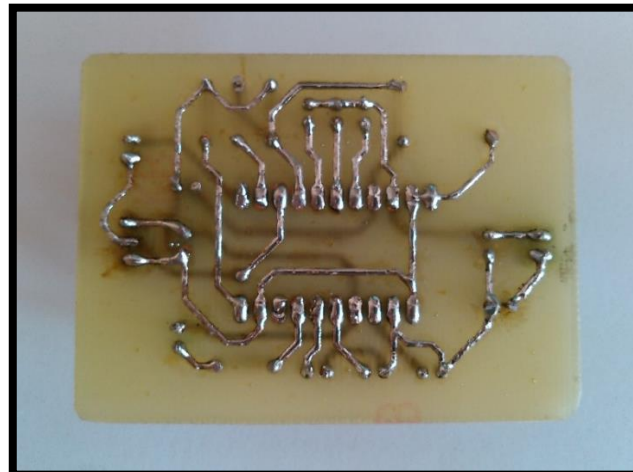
PCB del circuito del chip bq51050B final (BOTTOM)
